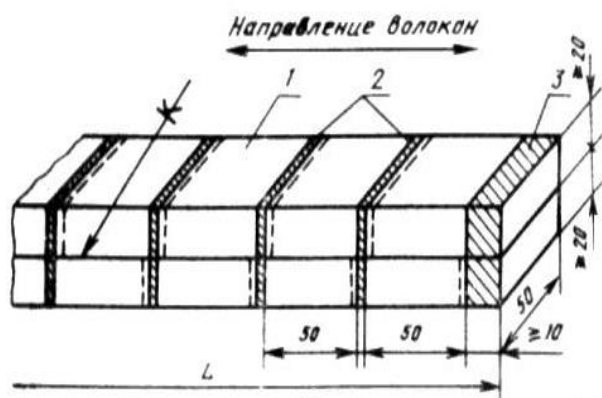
Схема изготовления образцов: 1 - заготовка для образца; 2-пропил; 3-припуск на обработку
